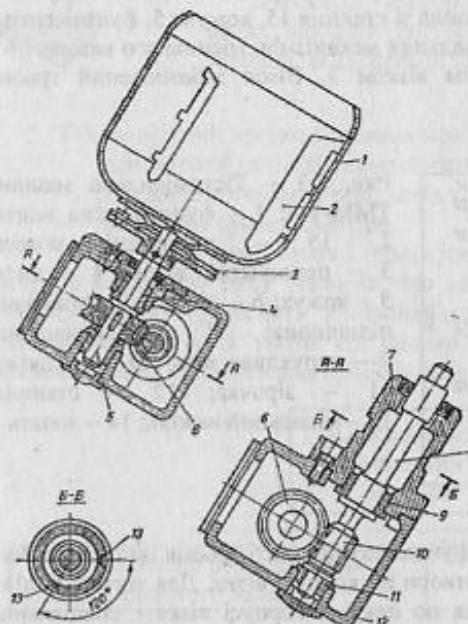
Механізм МС25-200 для перемішування овочів для салатів і вінегретів: 1 – бачок-барабан; 2 – ребра; 3 – фланець; 4 – втулки; 5 – вал; 6 – колесо черв'ячне; 7 – хвостовик; 8 – кільцева канавка; 9, 11 – втулки; 10 – черв'як; 12 – корпус редуктора; 13 – отвори, в які входять кінці гвинтів
